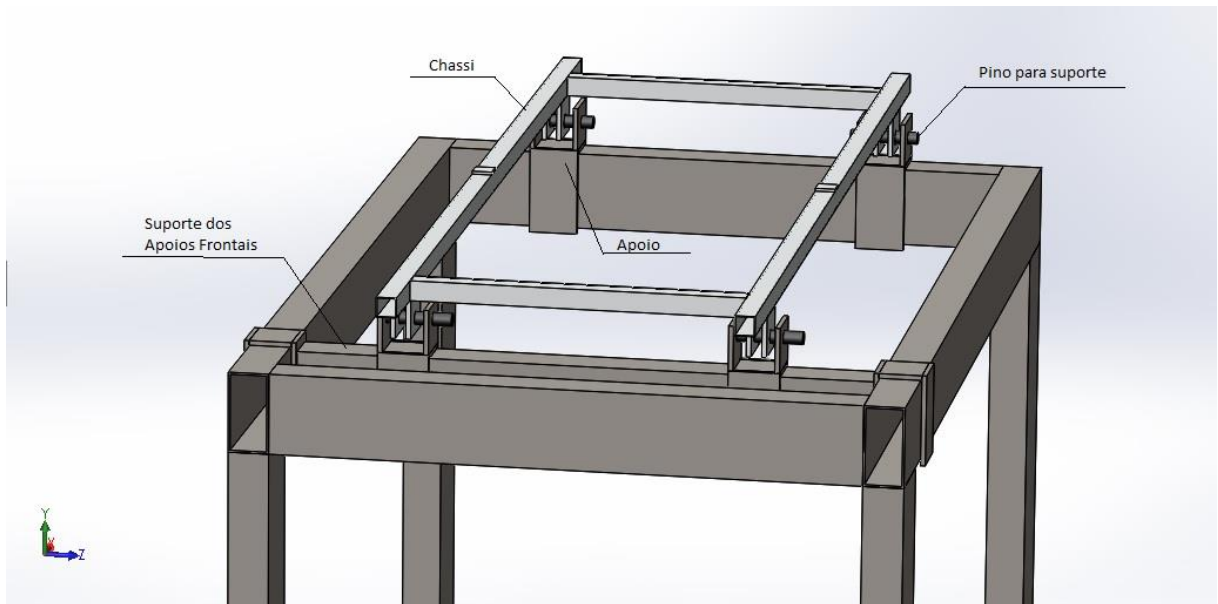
Chassi em posição de ensaio sobre a bancada - Modelo CAD
